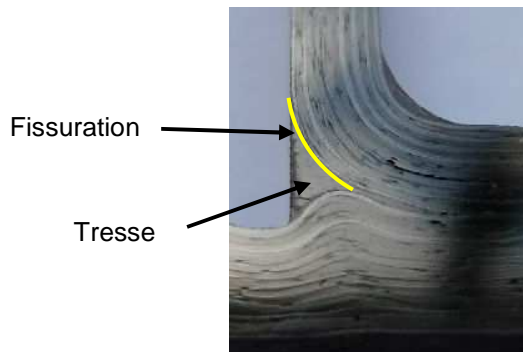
Position de la fissuration entre le pied de nervure et la peau
